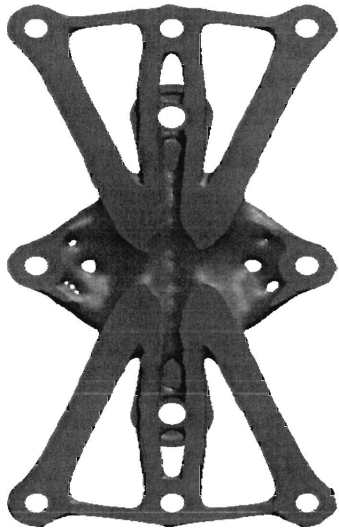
Vedere frontală element de prindere optimizat topologic CAD – TIP 1
